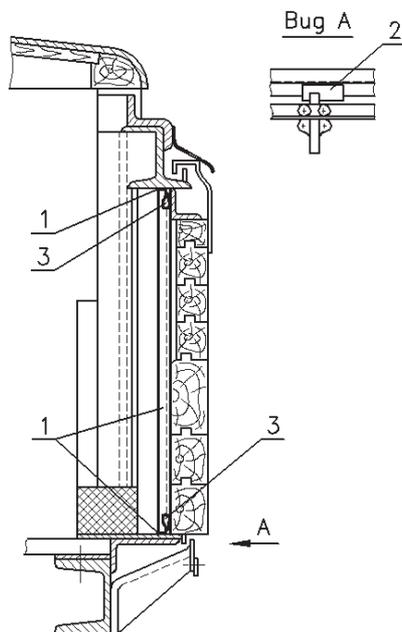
Заделка зазоров двери вагона, используемой для погрузки, бумагой
